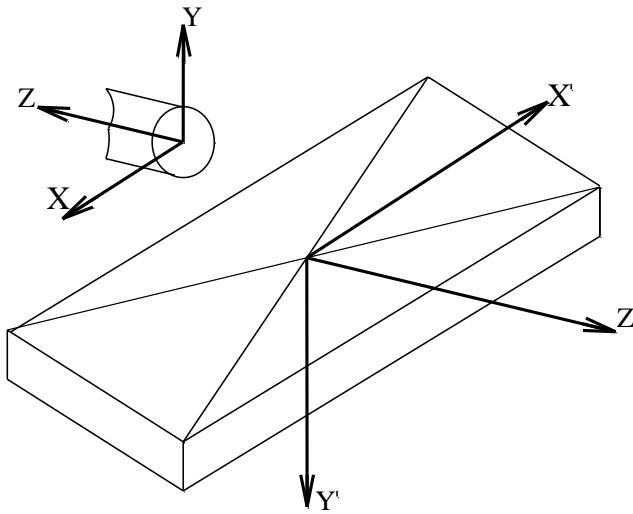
Позитивні напрямки осей для верстата з горизонтальною віссю обертання шпинделя
